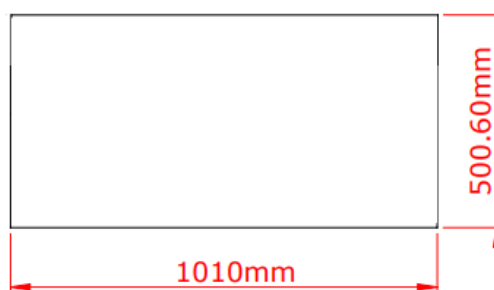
Sección 2 de la carcasa - Detalle de las medidas
